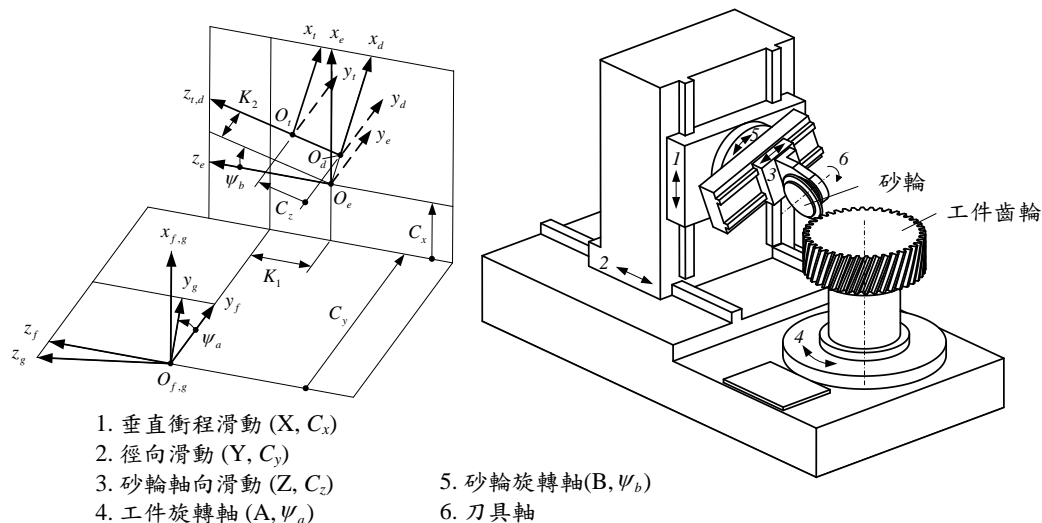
五軸 CNC 成形砂輪磨齒機坐標系統
